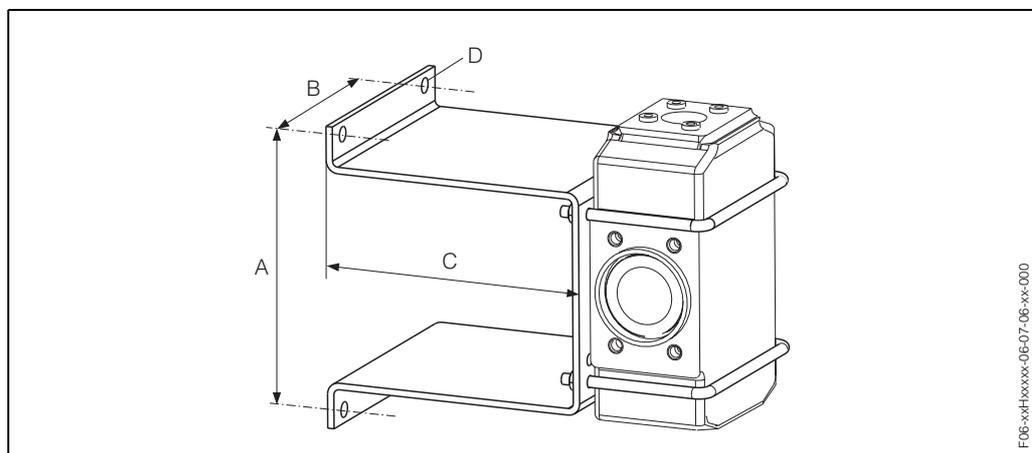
Kit per il montaggio a parete per H / DN 2...25
